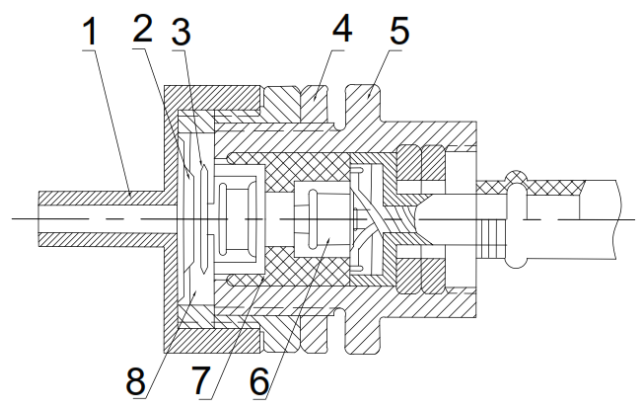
(б) Конструкция датчика давления ДД-6С: 1-штуцер; 2-мембрана; 3-ярмо; 4-гайка; 5-корпус; 6-катушка; 7-сердечник; 8-катушка
